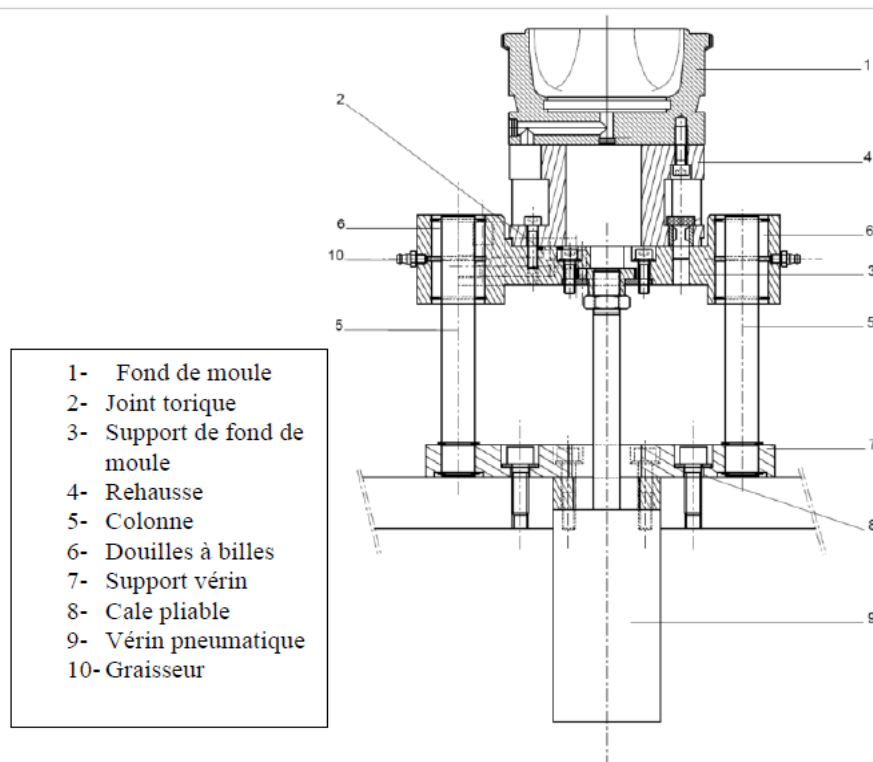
ond de moule de la souffleuse SBO4 [1]
